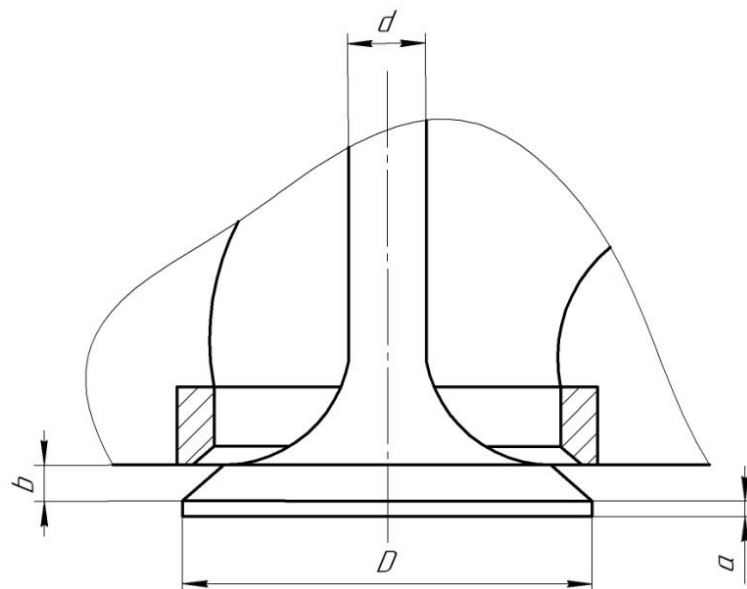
Профиль рабочей части выпускного клапана: D – диаметр тарелки клапана; a – ширина верхней вспомогательной фаски; b – ширина рабочей фаски; d – диаметр стержня
